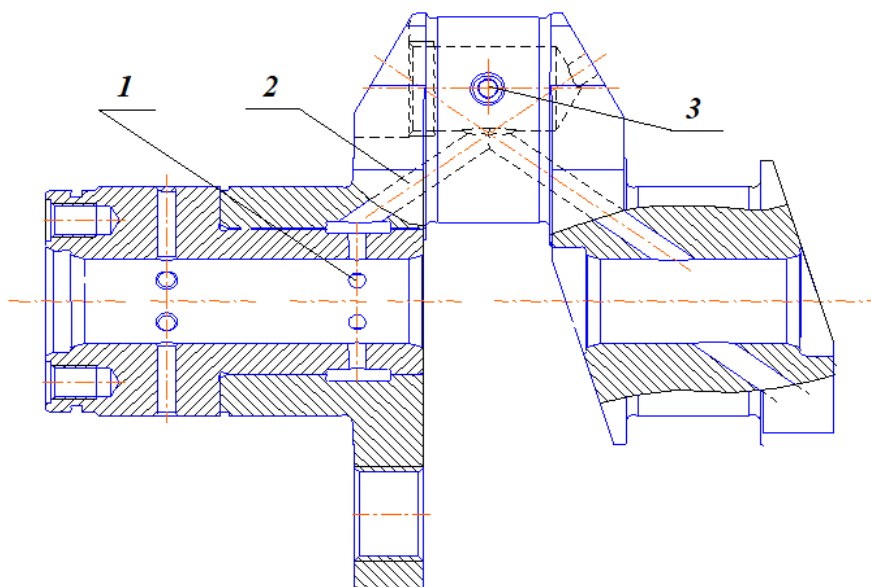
Схема подачи смазки в шатунный подшипник двигателя 4Т371:
